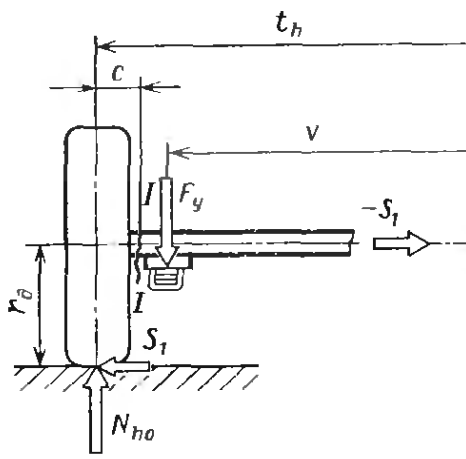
В трубчатой балке неразрезной оси опасное сечение $I-I$, как правило, расположено возле сварного шва, которым закреплена опора продольной листовой рессоры
